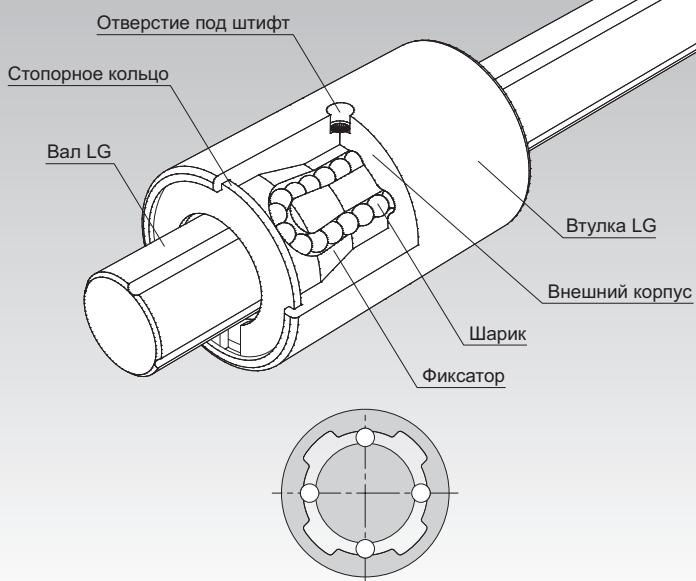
Конструкция шариковой втулки с направляющей модели LG
